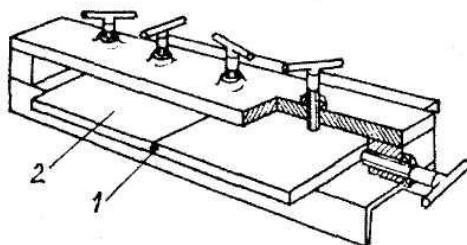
Приспособление для сборки пластин: 1 — прихватка; 2—пластина.
